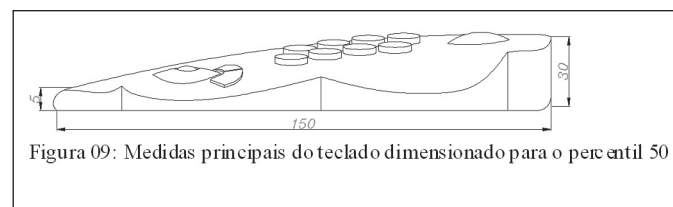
Medidas principais do teclado dimensionado para o percentil 50
